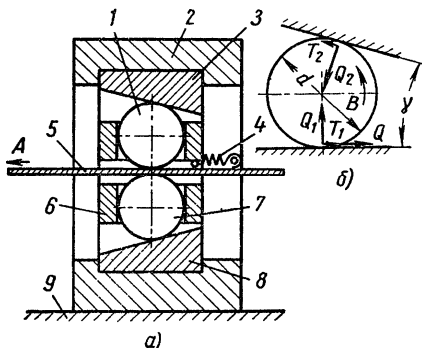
Конструкція (а) і розрахункова (б) схема роликово-клинового захвату
